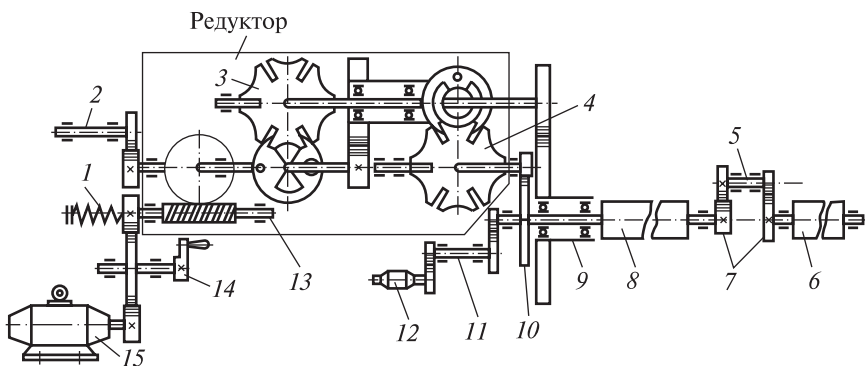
Кинематическая схема контроллера ЭКГ-8:
